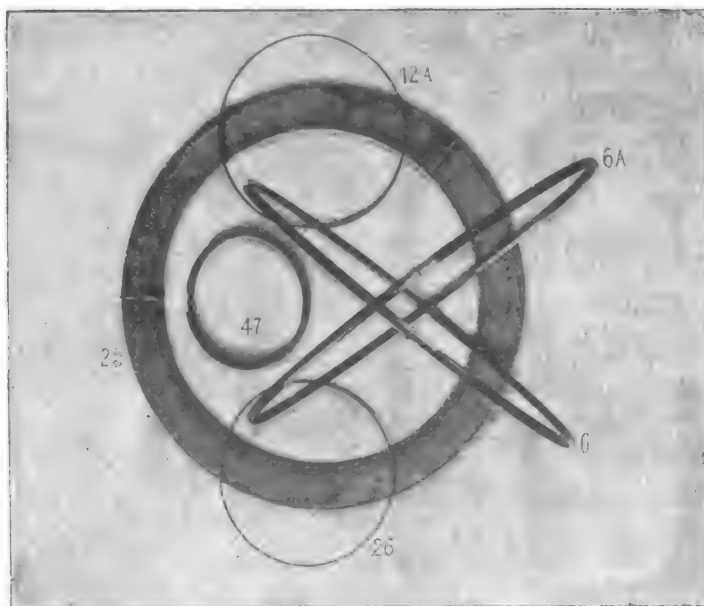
Cercles soudés à la machine électrique.
